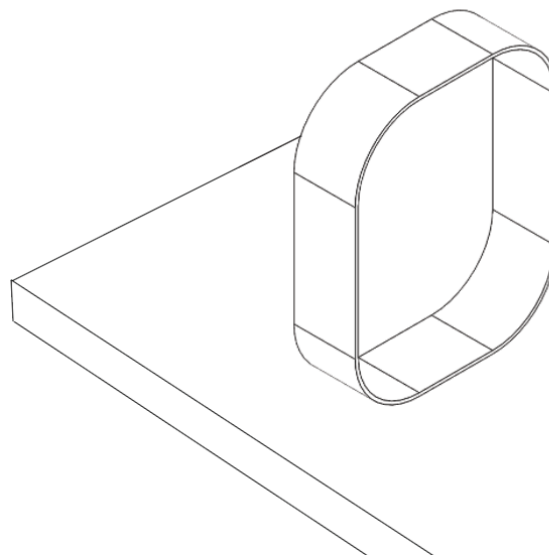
Secuencia 5. Ensamblaje 1.1.1.1.1
